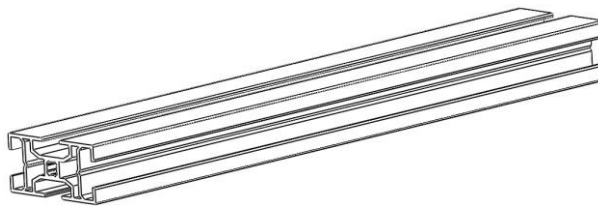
Detalhe do perfil 50x25 mm, em alumínio 6060-0 para as barras longitudinais superiores e barras transversais, na estrutura de base do actuador (perspectiva dimétrica).
